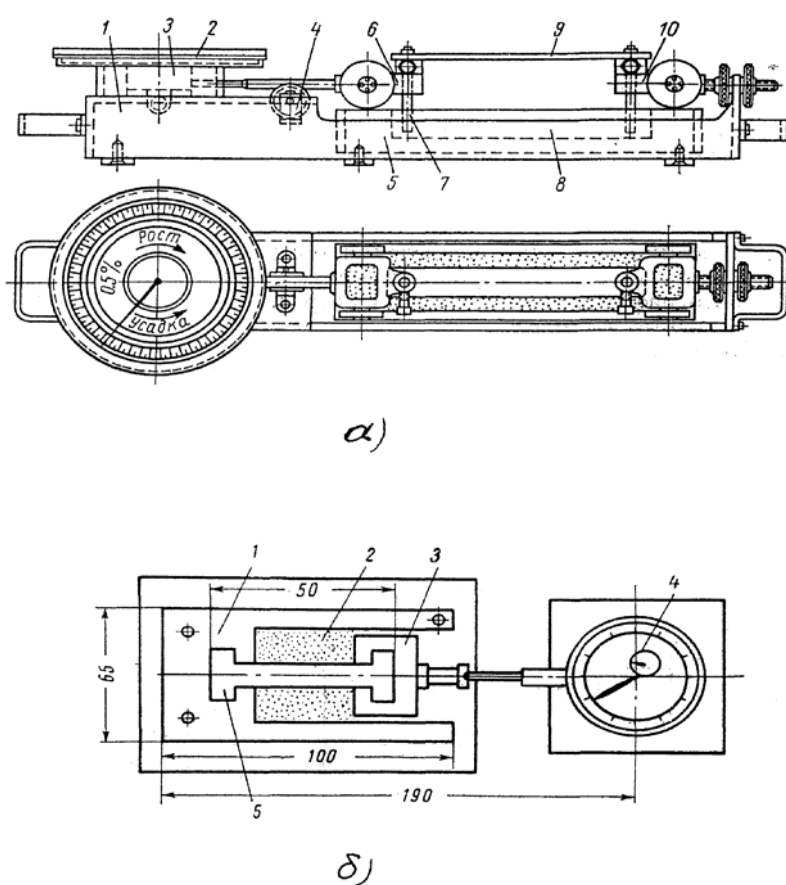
Приборы для определения линейной усадки: а – прибор конструкции И.Ф. Большакова; б – прибор конструкции А.А. Бочвара
